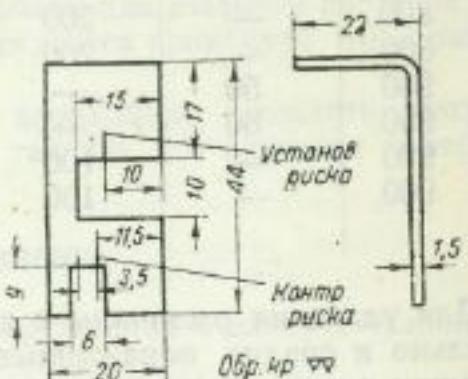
Калибр сборочный для проверки положения барабана $\frac{\text{Д}}{\text{ПМ-65}}$. Ст. 6,
